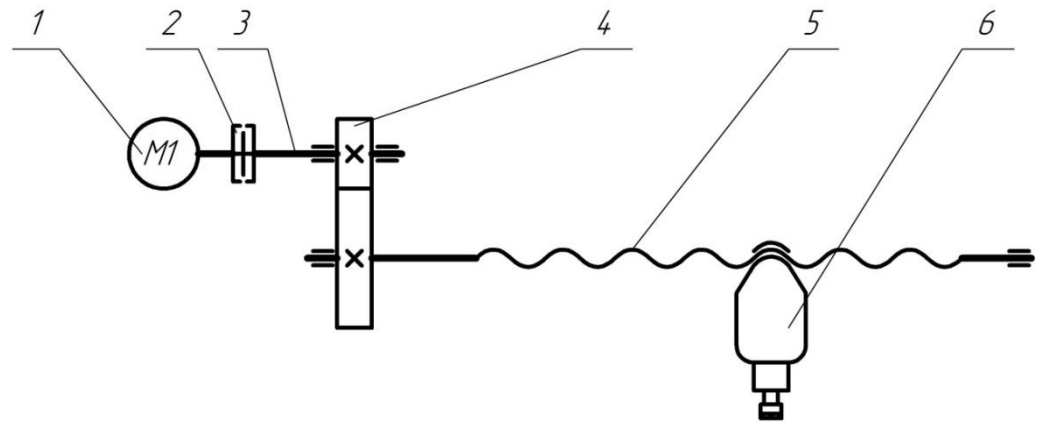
Орієнтована кінематична схема приводу силової фрезерної голівки: 1 – Електродвигун; 2 – дискова двостороння муфта зчеплення; 3 – вал; 4 – редуктор; 5 – Нерозмірна передача «гвинт-гайка»; 6 – силова фрезерна голівка.
